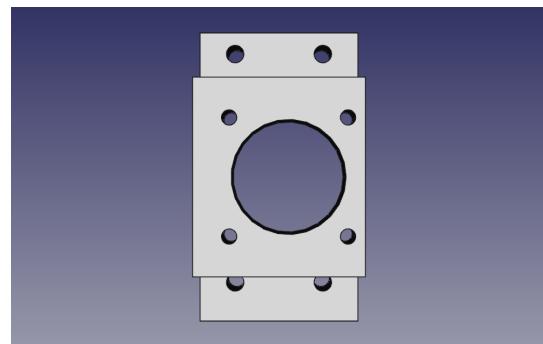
Imagen del perfil de la pieza de sujeción del motor.
